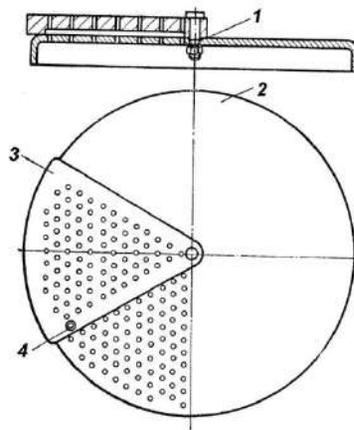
Схема установки кондуктора при сверлении трубной решетки: 1 – опорный болт; 2 – заготовка решетки; 3 – кондуктор; 4 – установочный штифт
